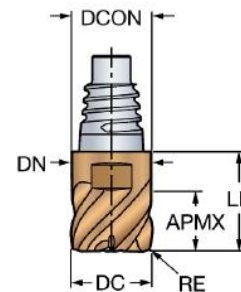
Cap de frezat din carbură metalică 316-16FM650-16015L 1030 [3]
